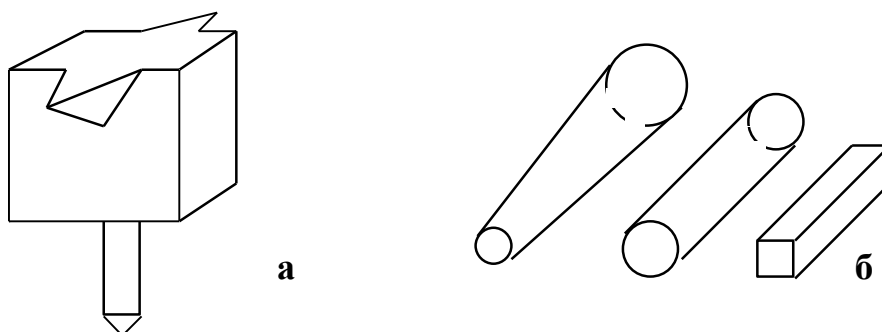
Двурогая наковальня - шперак(а) и ригели (б): конический, цилиндрический, квадратный
